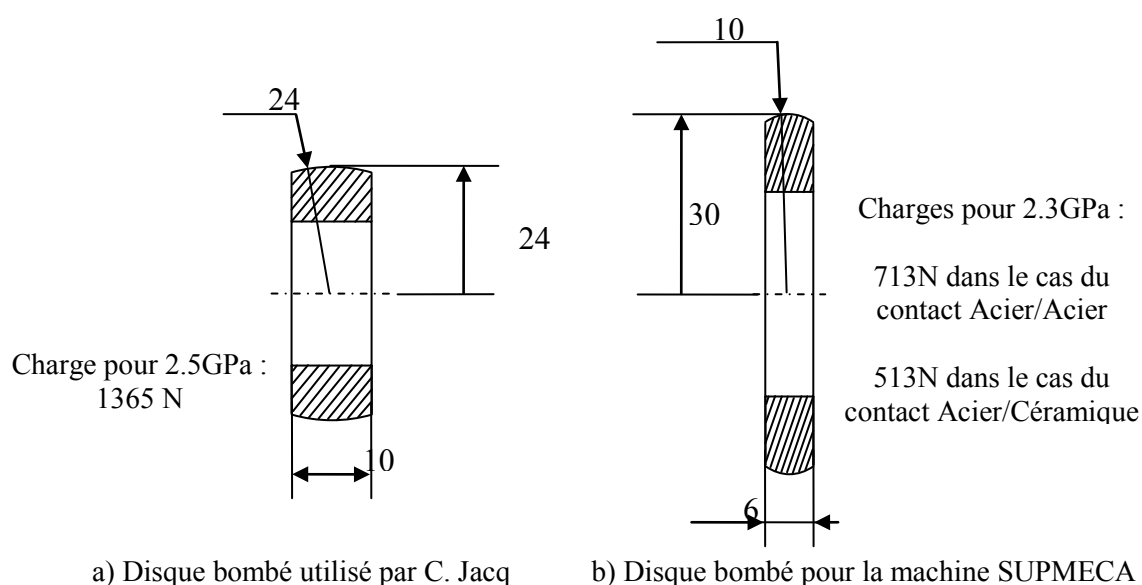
Géométrie des éprouvettes bombées des deux machines bi-disques
